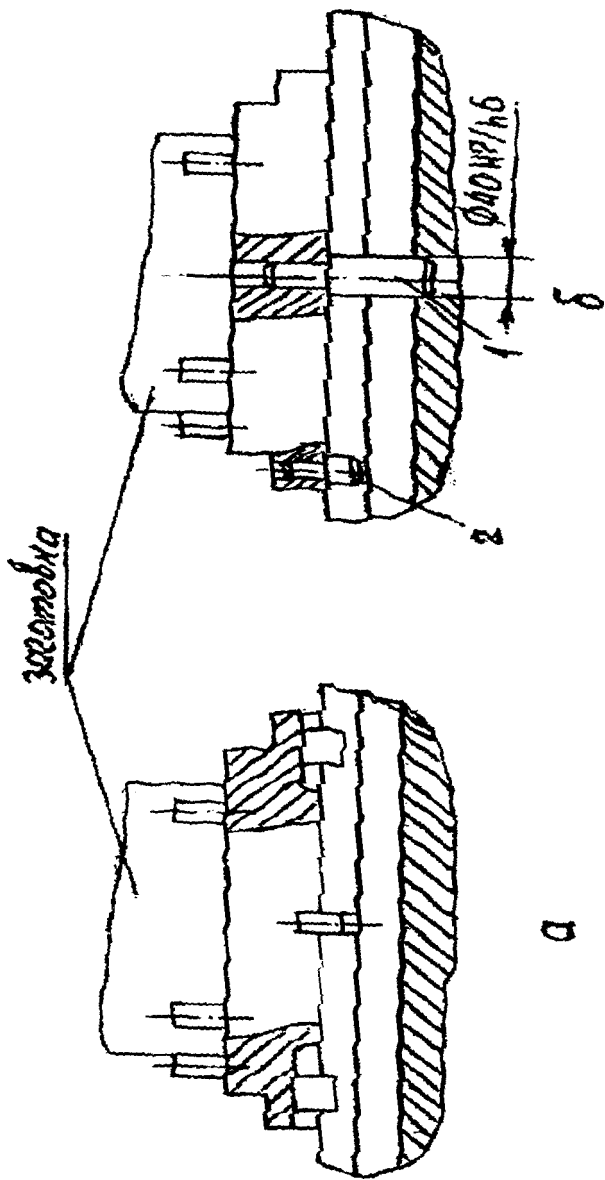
Схемы базирования приспособлений на станках с ЧПУ: а - шпонками по продольному и поперечному пазам; б - штырями по центральному отверстию и продольному пазу
